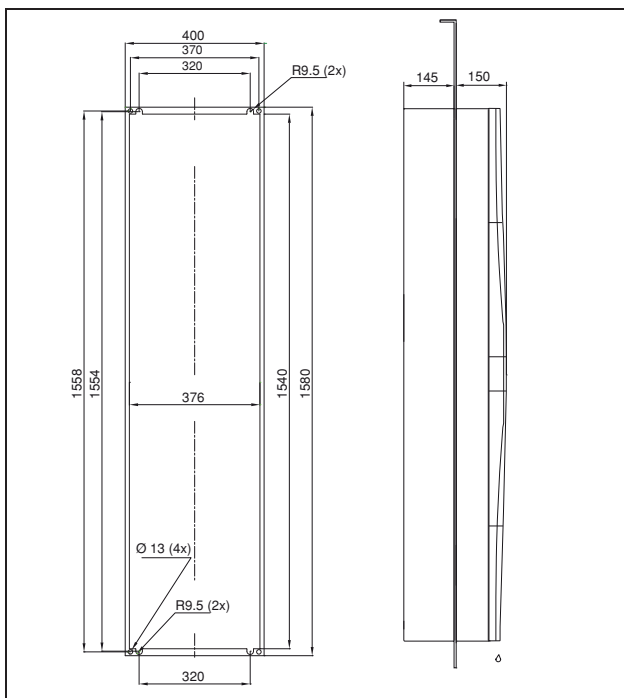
3328.xxx, 3329.xxx delinbyggnad
